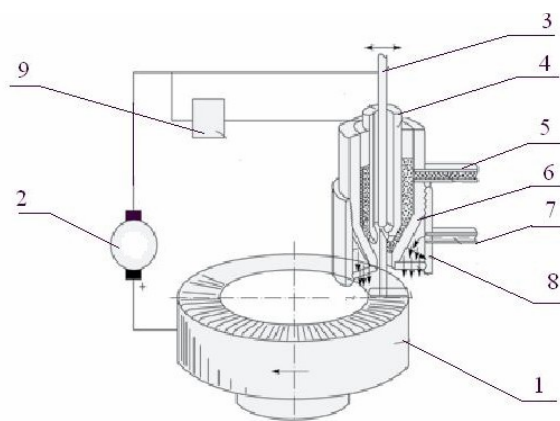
Схема плазменно-порошковой наплавки: 1 – изделие; 2 – источник питания плазменной дуги; 3 – вольфрамовый электрод; 4 – стабилизирующее сопло плазмотрона; 5 – ввод транспортирующего газа с порошком; 6 – фокусирующее сопло; 7 – ввод защитного газа; 8 – защитное сопло; 9 – устройство поджига дуги
